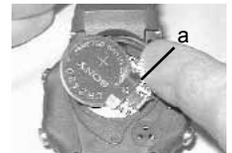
EXTRACCIÓN DE LA BATERÍA
